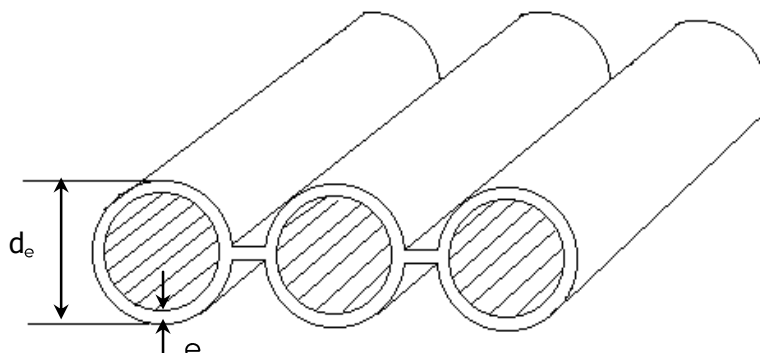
Corte de uma secção reta de Tritubo DN 40
